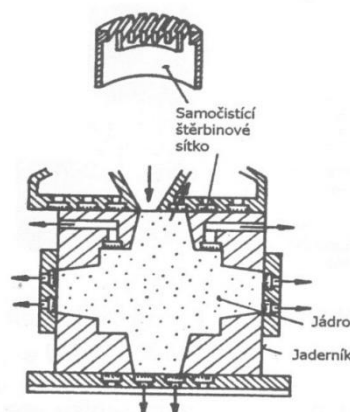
Hliníkový horizontálně dělený jaderník s epoxidovou výstelkou
